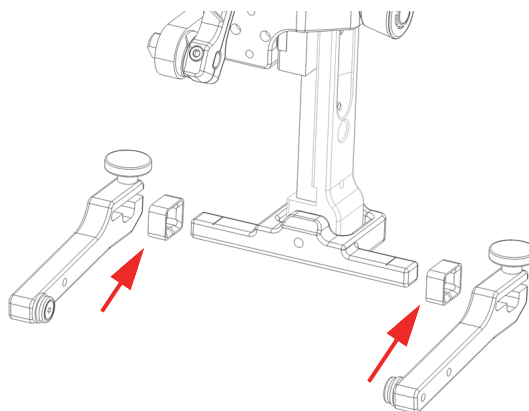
Снятие рычагов вилки и установка прокладок
